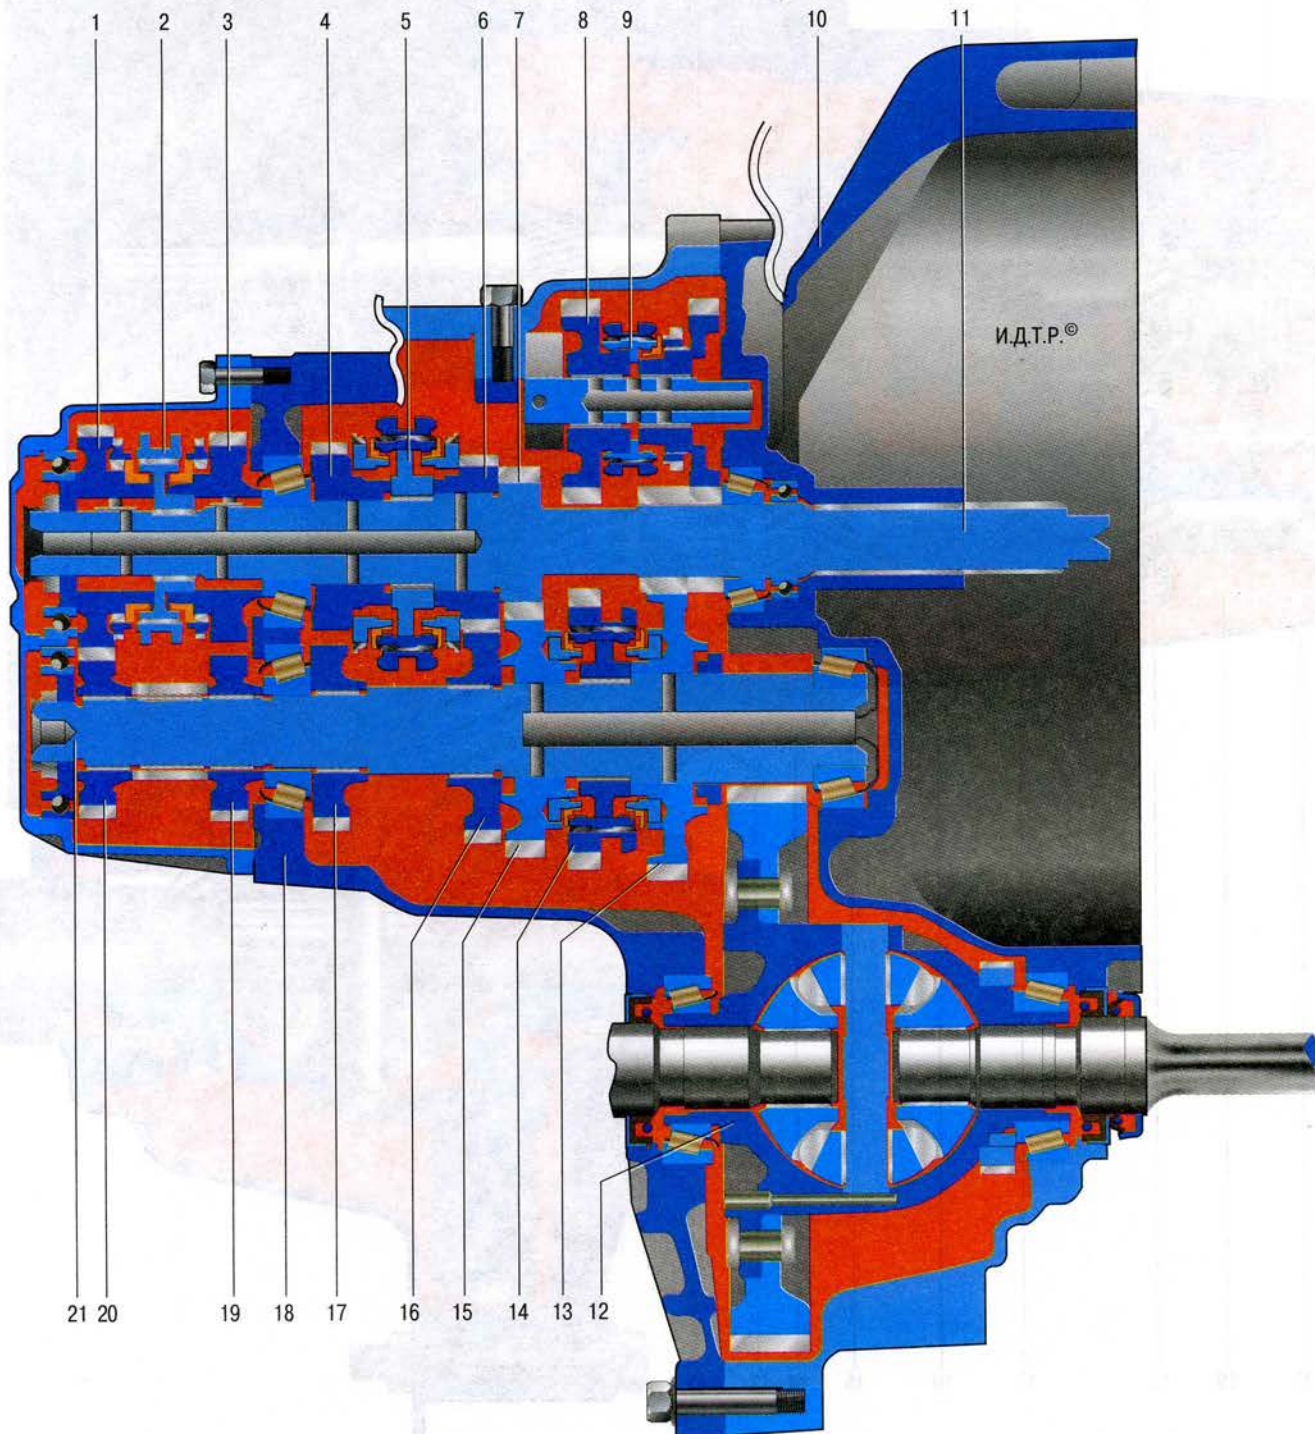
Принципиальная схема шестиступенчатой механической коробки передач мод. G66M-R: 1 – ведущая шестерня VI передачи; 2 – муфта V и VI передач; 3 – ведущая шестерня V передачи; 4 – ведущая шестерня IV передачи; 5 – муфта III и IV передач; 6 – ведущая шестерня III передачи; 7 – ведущая шестерня II передачи; 8 – промежуточная шестерня заднего хода; 9 – муфта передачи заднего хода; 10 – картер сцепления; 11 – первичный вал; 12 – дифференциал; 13 – ведомая шестерня I передачи; 14 – муфта I и II передач и шестерня заднего хода; 15 – ведомая шестерня II передачи; 16 – ведомая шестерня III передачи; 17 – ведомая шестерня IV передачи; 18 – картер коробки передач; 19 – ведомая шестерня V передачи; 20 – ведомая шестерня VI передачи; 21 – вторичный вал
